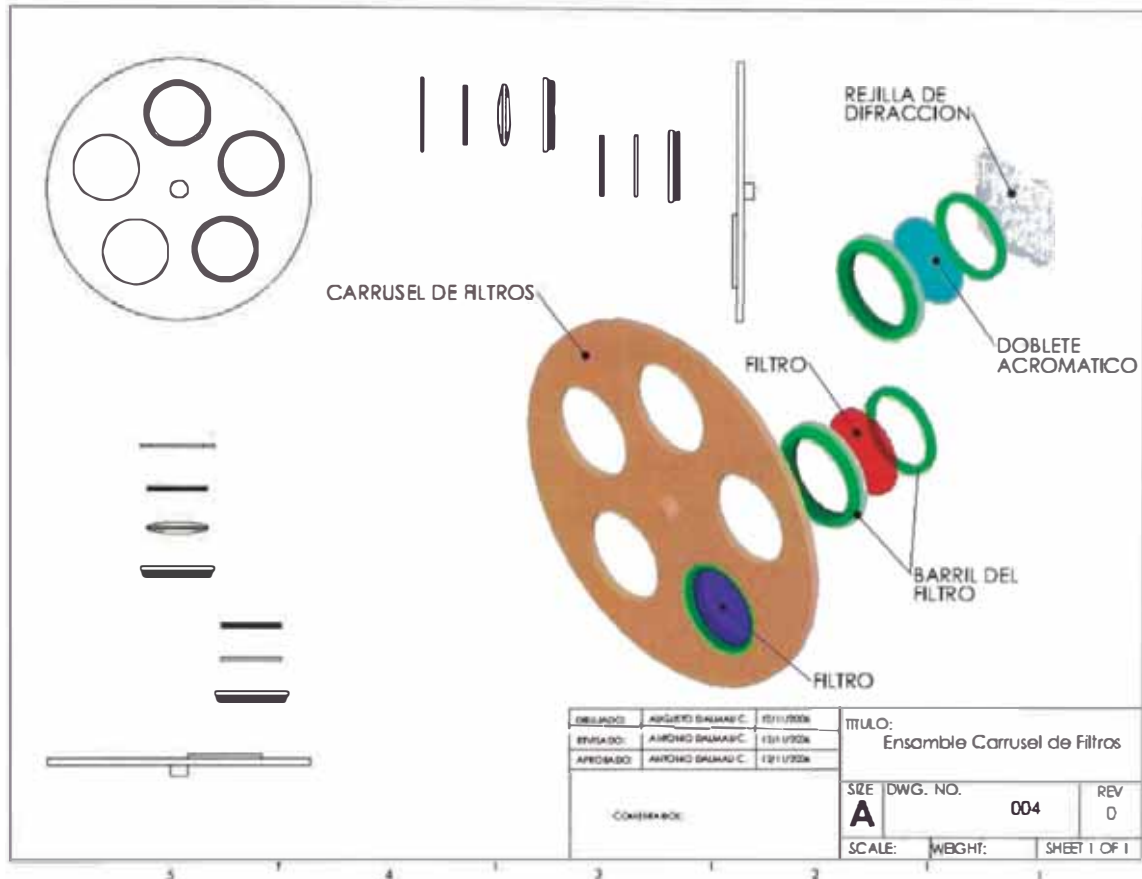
Montaje del sistema dispersor en un barril para filtros
